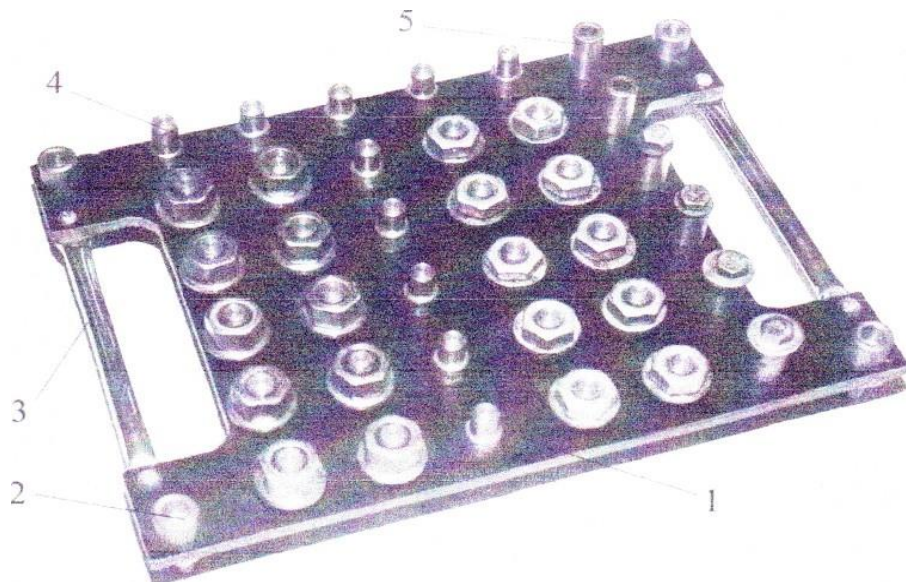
Касета для кріпильних виробів: 1 - плита; 2- ніжки; 3 - ручка; 4- базові штирі для шайб і гайок; 5 - базові гнізда для болтів з шайбами.
